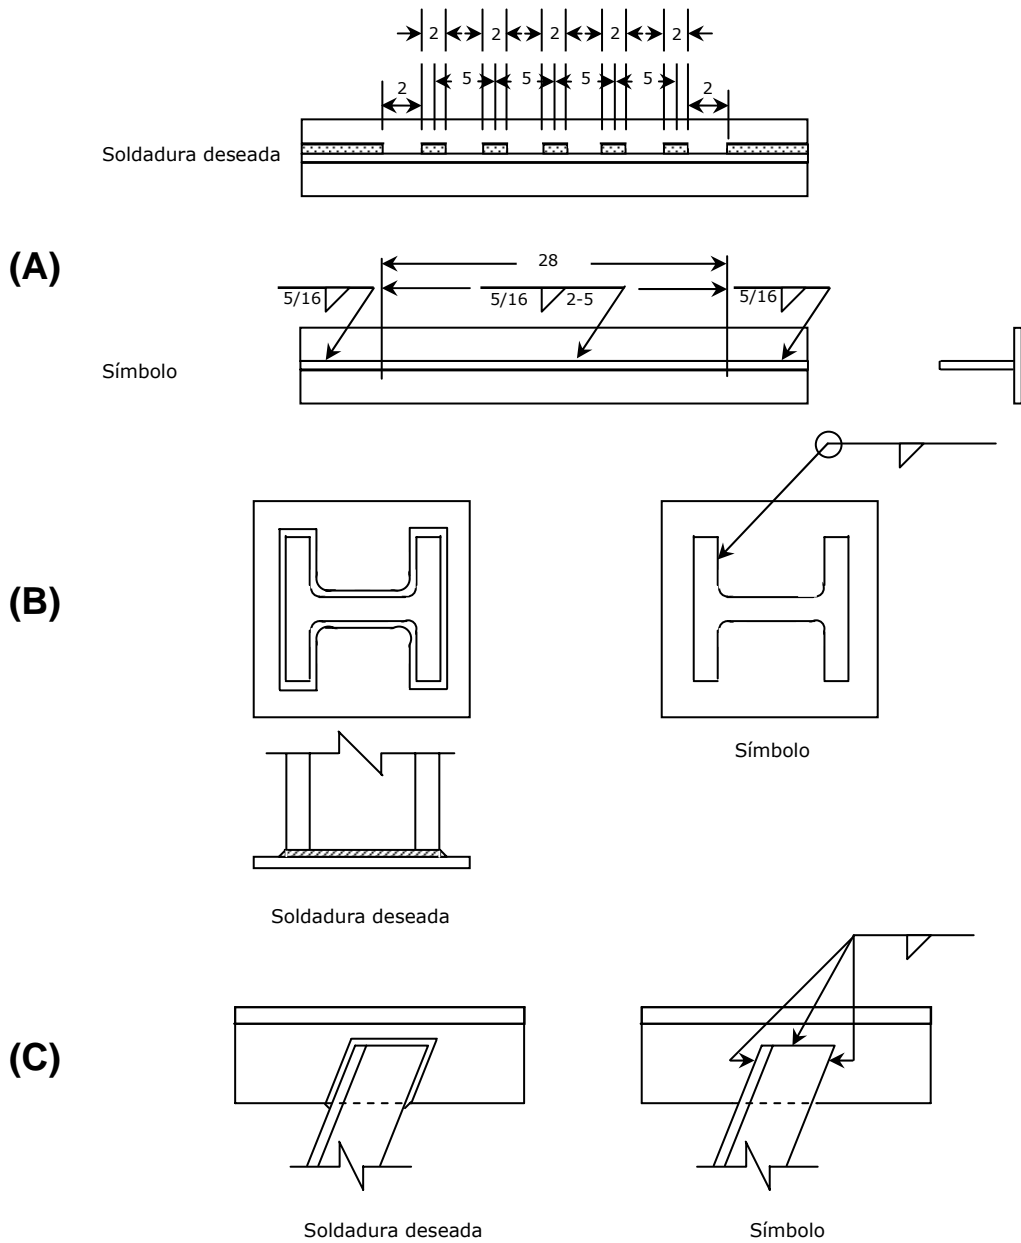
Símbolos para aplicación de soldadura en diferentes direcciones
